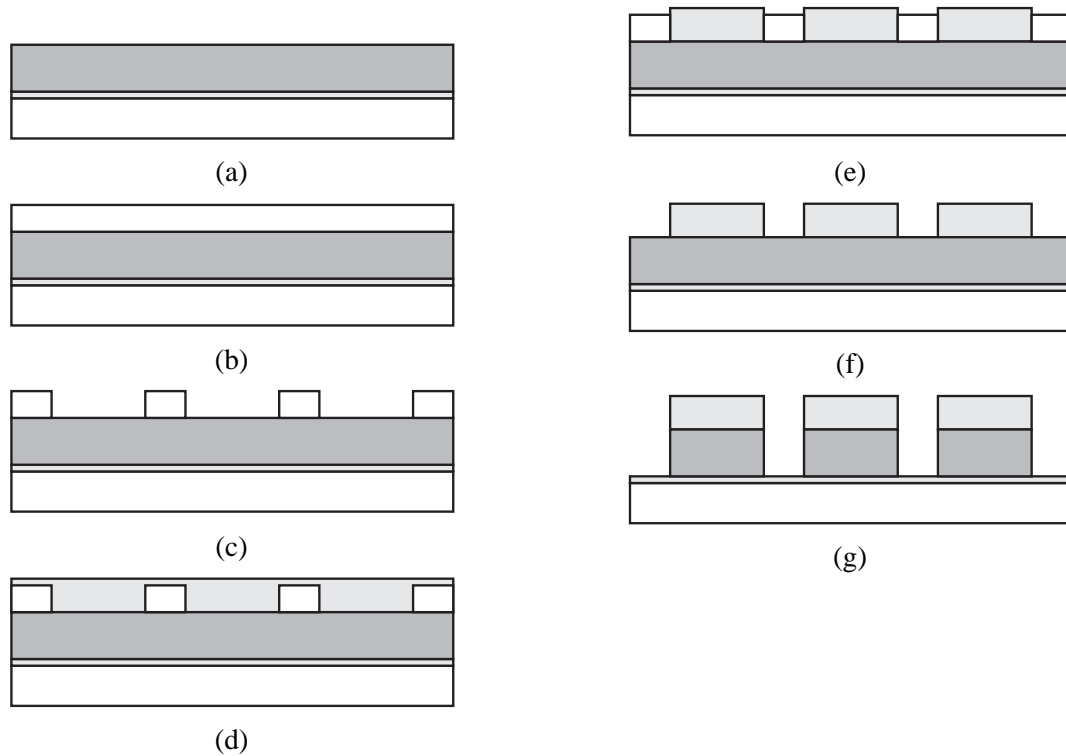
Étapes de l'usinage avec un masque en élastomère de silicone moulé. (a) Le PZT (gris foncé) est collé sur un support. (b) et (c) Création du moule de SU-8 par un procédé de lithographie (LIGA-UV). (d) Moulage du masque en élastomère de silicone. (e), (f) et (g) Micro-sablage proprement dit.
